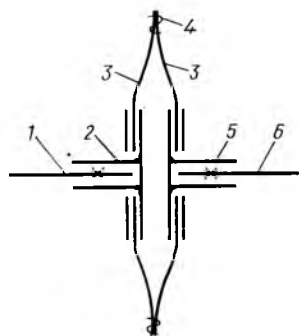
Конструкция эластичной муфты: 1 — вал контрпривода; 2 — ведомая полумуфта; 3 — кольца из транспортерной ленты; 4 — шкива колен; 5 — ведущая полумуфта; 6 — вал электродвигателя
